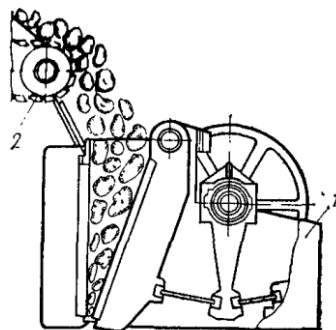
Схема загрузки щековой дробилки:
